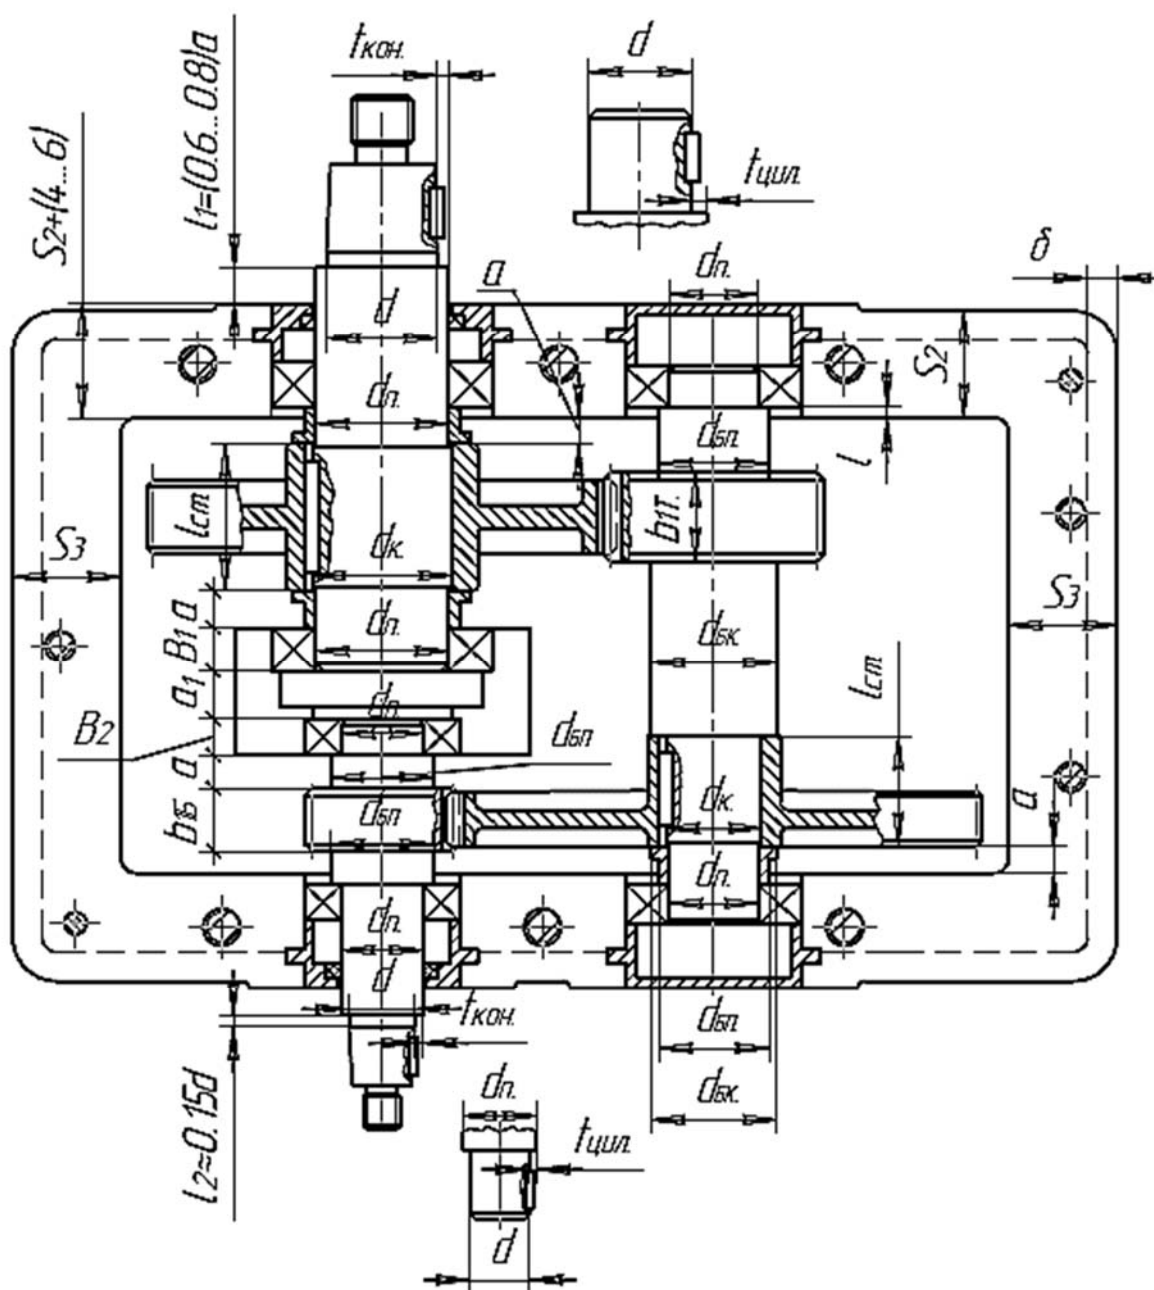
Компоновка цилиндрического двухступенчатого соосного редуктора с внутренним расположением подшипниковых бобышек
